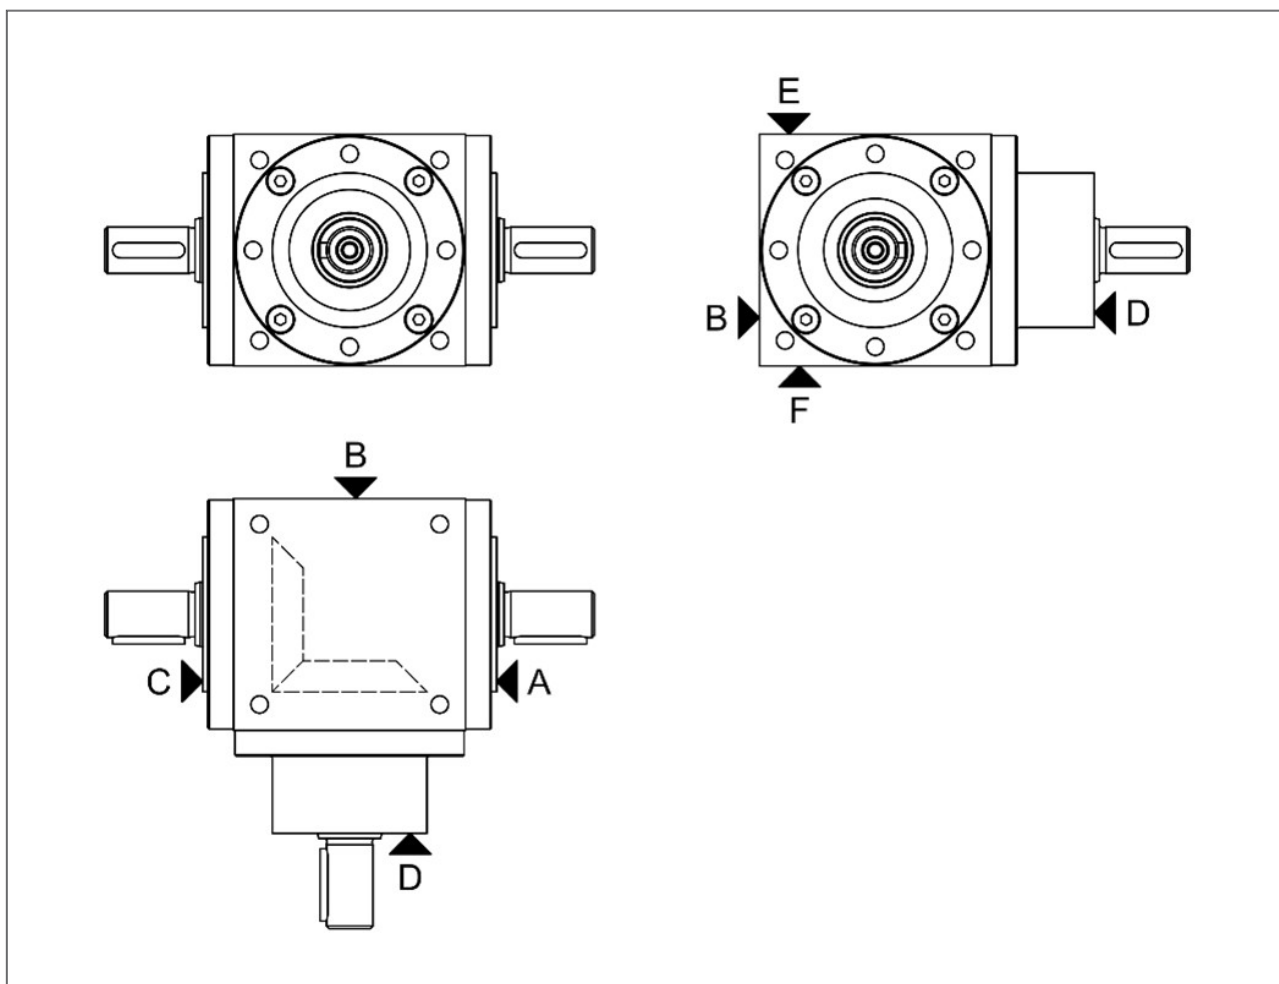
Vista general del reductor de engranajes cónicos ZK de ZIMM
